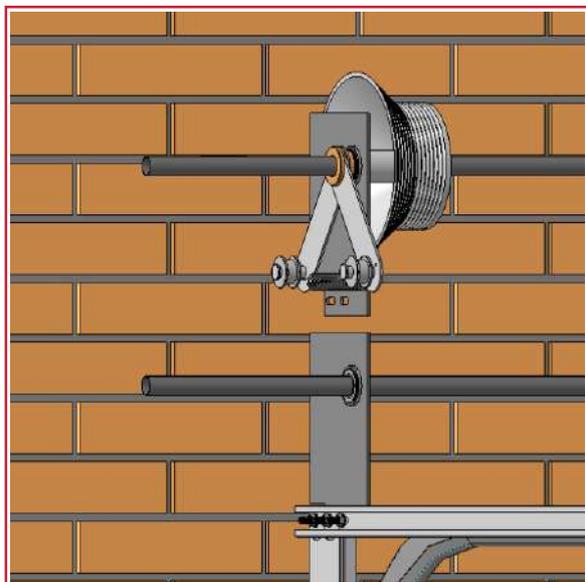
Установка цепного привода на двухвальной системе с расположением устройства натяжения цепи изнутри
